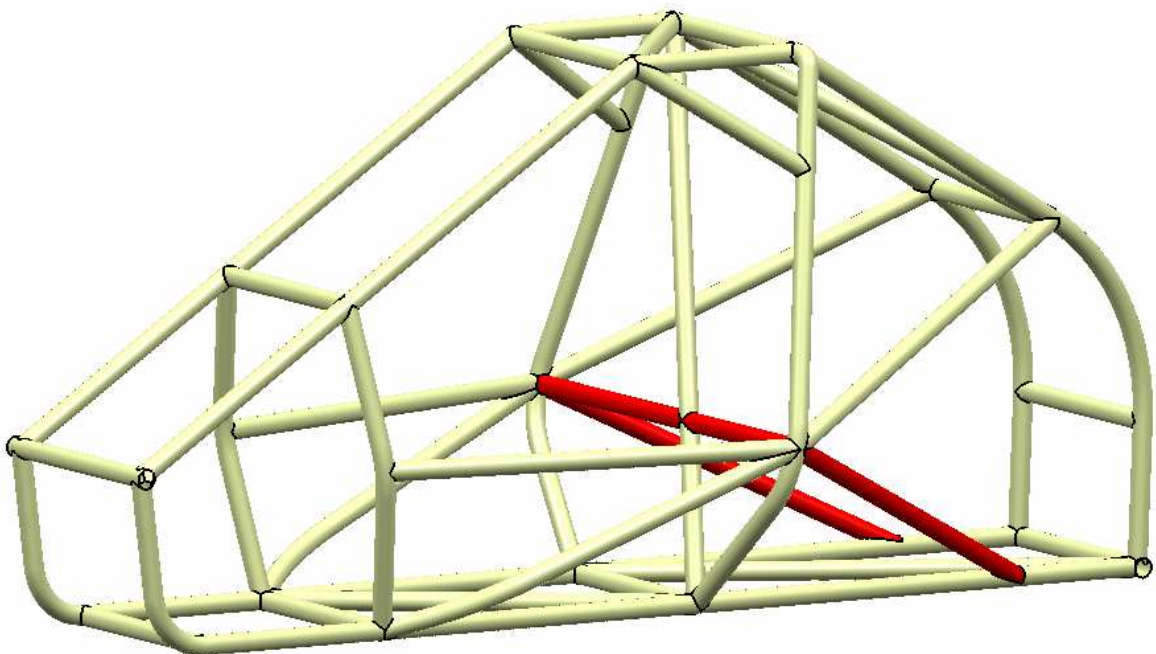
Estructura reforzada. Fuente: elaboración propia.
